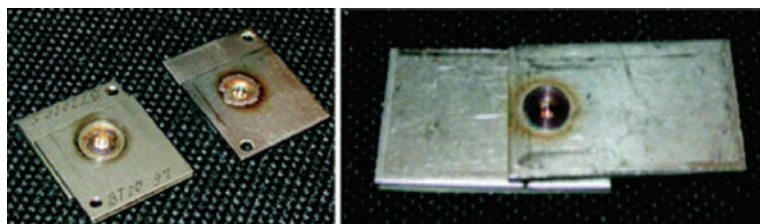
Образцы из титанового сплава ВТ20 и стали 12Х18Н10Т, сваренные точечной СТП.
